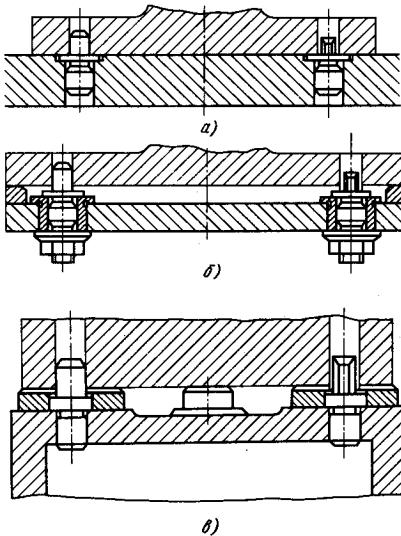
Установка заготовки двумя цилиндрическими отверстиями с параллельными осями и перпендикулярной к ним плоской поверхностью с использованием стандартизованных установочных пальцев: а - по ГОСТ 12209-66, и ГОСТ 12210-66; б - по ГОСТ 12211-66 и ГОСТ 12212-66; в - по ГОСТ 17774-72 и ГОСТ 17775-72
